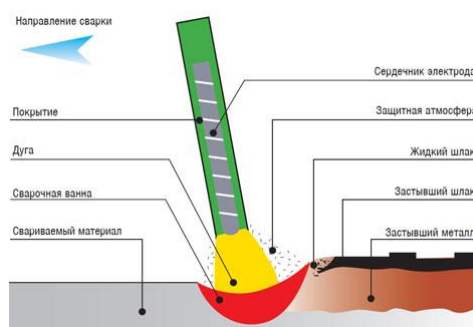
Ручная дуговая сварка металла покрытым электродом [3]
